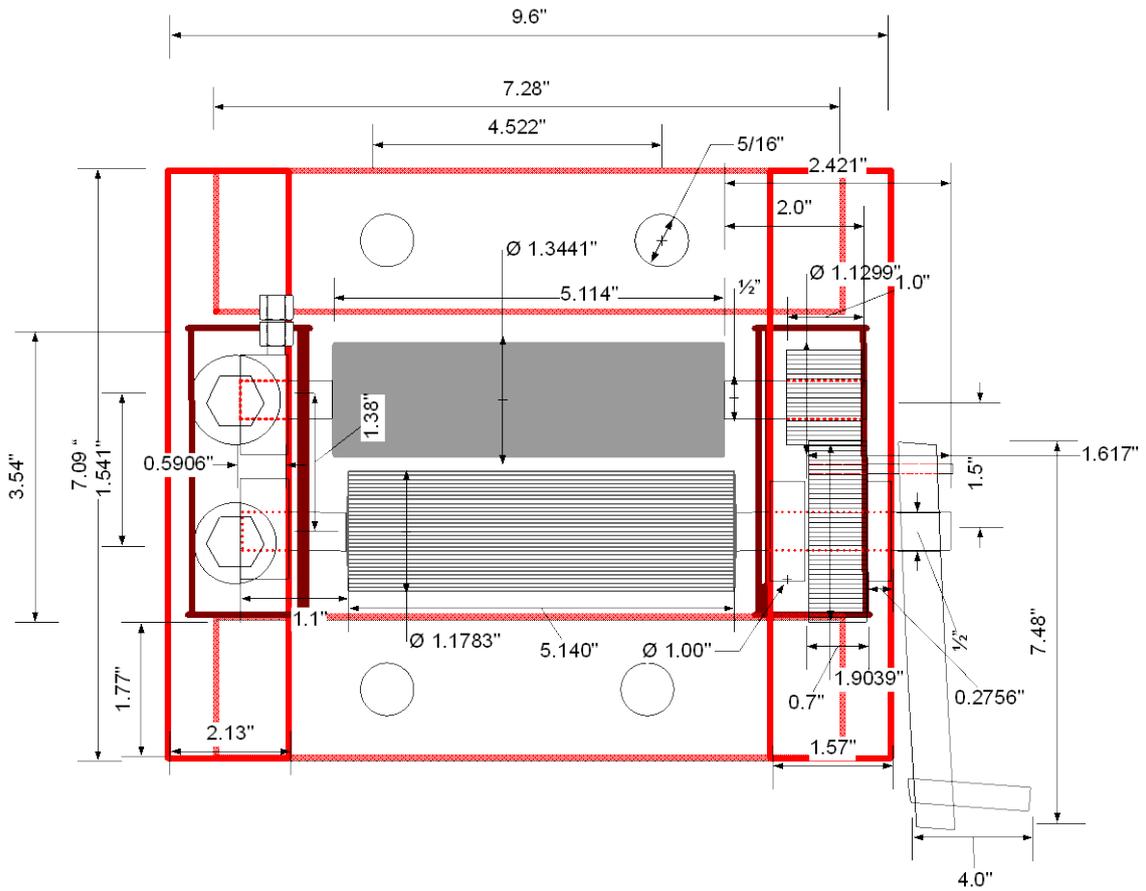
Dimensiones de la máquina quebradora de piñón, Vista superior sin la tova y cubierta.
